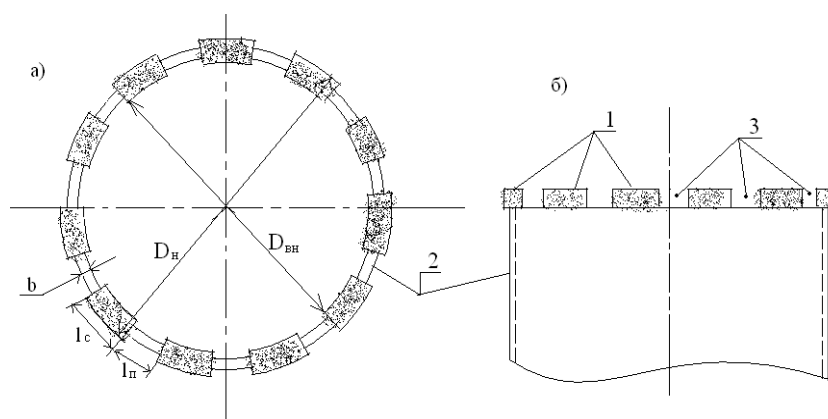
Кольцевое алмазное сверло с прерывистой рабочей поверхностью: 1 – алмазоносный сегмент; 2 – корпус сверла; 3 – зазор между сегментами; D_n – наружный диаметр сверла; $D_{вн}$ – внутренний диаметр сверла;
